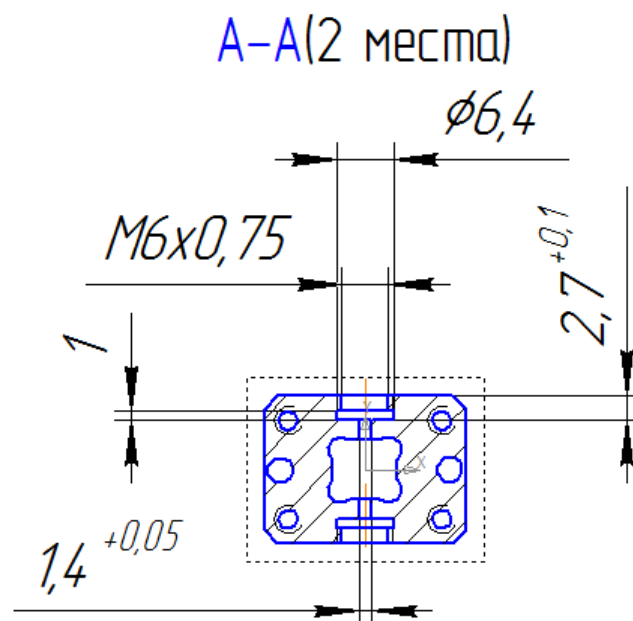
Расстановка размеров, обозначений и допусков
